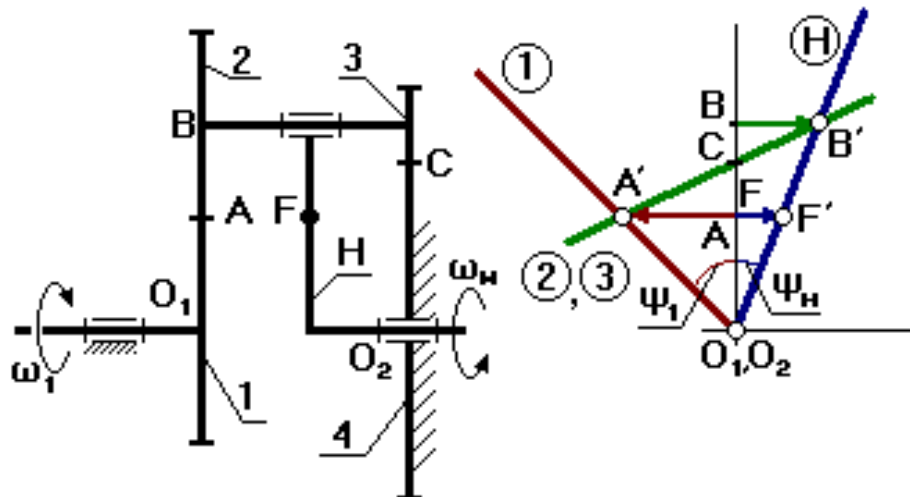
Редуктор Давида: 1,2 – внешняя зубчатая пара, 3 – колесо, 4 – коронная шестерня, H - водило
